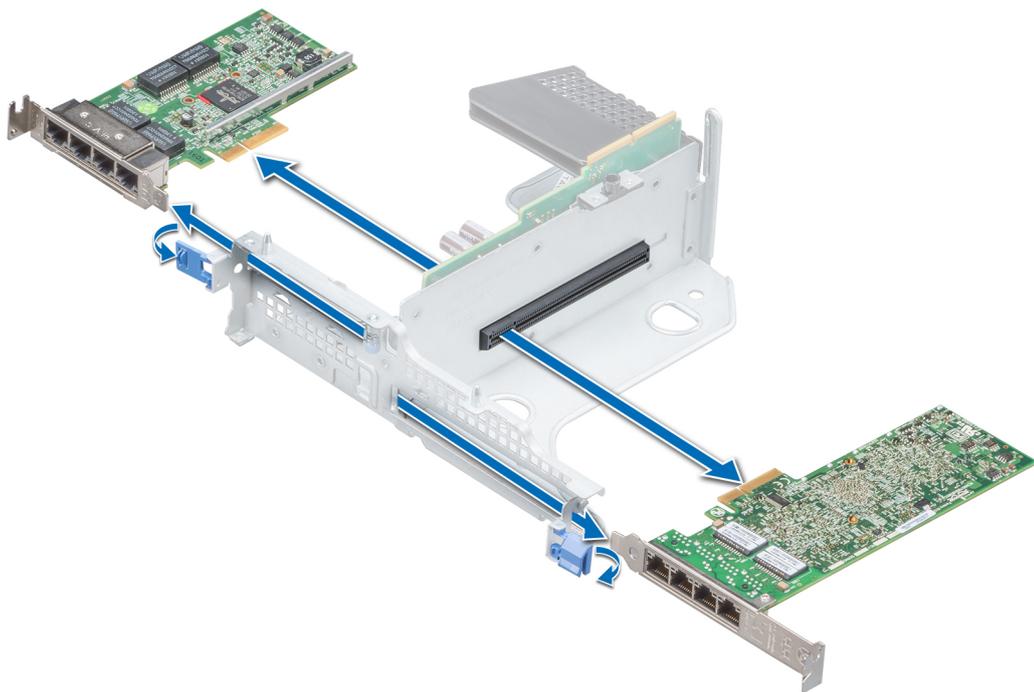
Entfernen einer Erweiterungskarte aus einem Butterfly Riser
